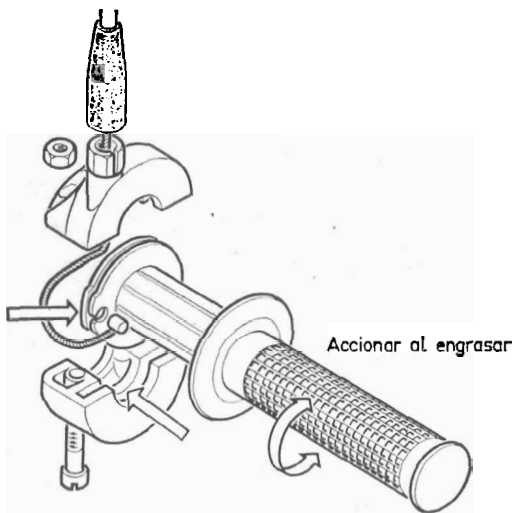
Puño de gas: Engrase y cambio del cable-funda.
